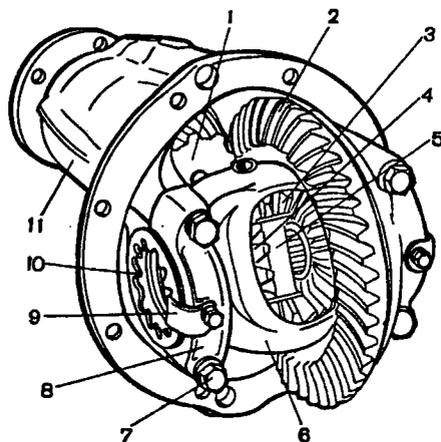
Редуктор заднего моста в сборе: 1 - ведущая шестерня; 2 - ведомая шестерня; 3 - сателлит; 4 - шестерня полуоси; 5 - ось сателлитов; 6 - коробка дифференциала; 7 - болты крепления крышки коробки дифференциала; 8 - крышка подшипника коробки дифференциала; 9 - пластина стопорная; 10 - регулировочная гайка подшипника; 11 - картер редуктора
